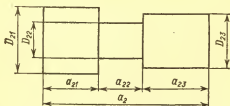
Эскиз цилиндрической заготовки со ступенчатым изменением диаметра
